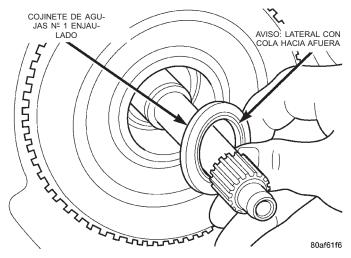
Desmontaje del cojinete de agujas enjaulado
